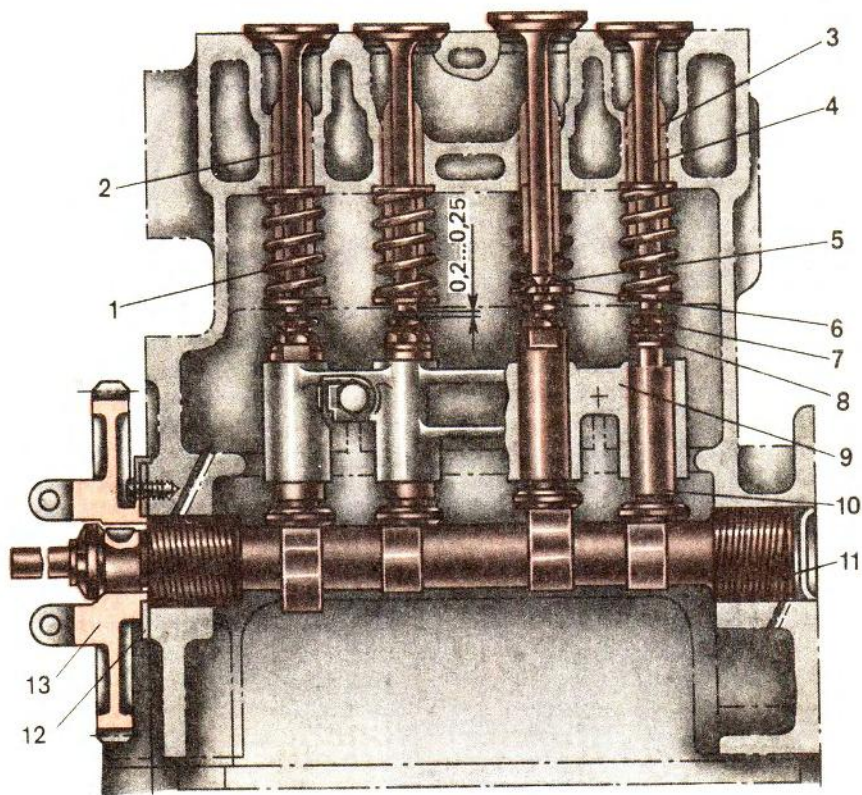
Механизм газораспределения с боковыми клапанами двигателя П-23У:
